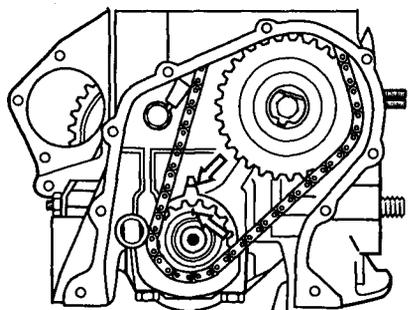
Положение установочных меток на звездочке коленчатого вала и блоке цилиндров (указаны стрелками)
